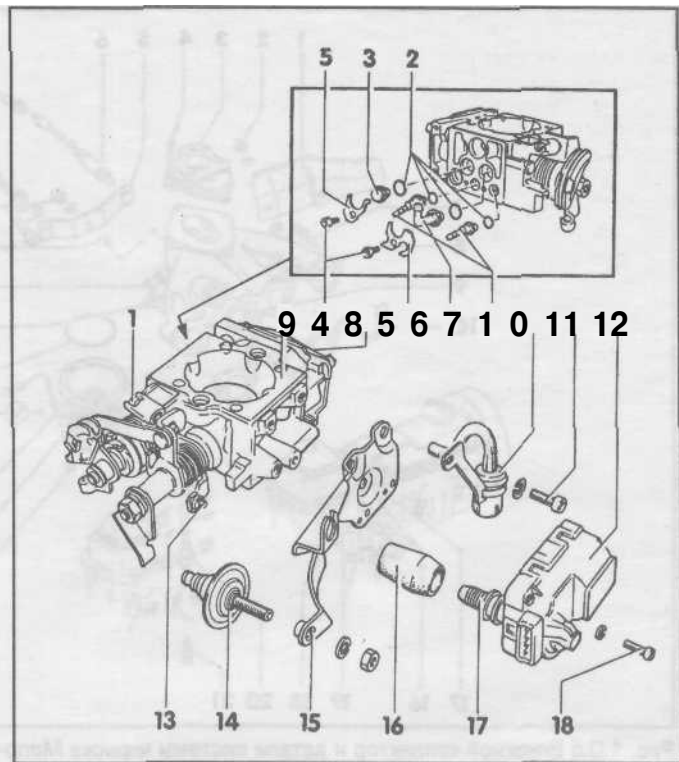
Нижний корпус блока форсунки и соответствующие детали
